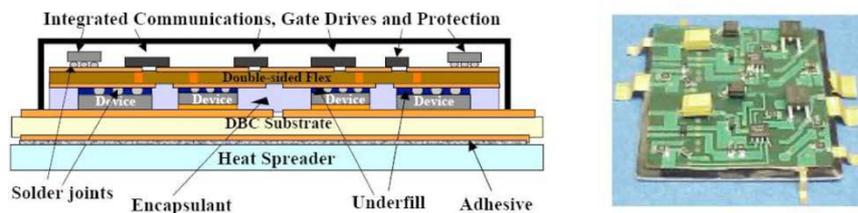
Module de puissance Flip chip on Flex utilisant la technologie solder bumps [56].
